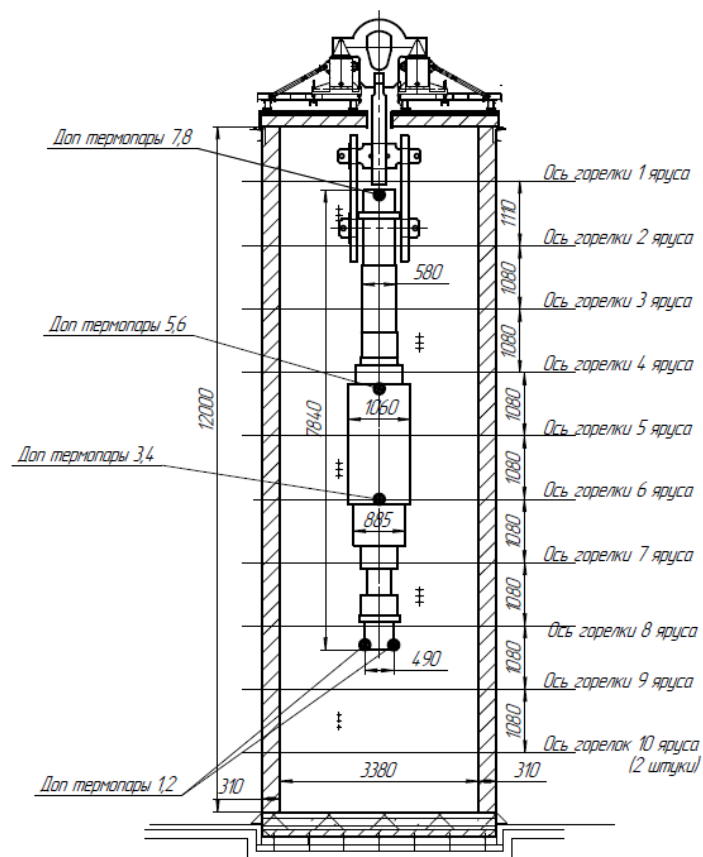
Конструкция печи № 22 с установкой опытного ротора массой 27,26 т, и размещение основных (печных) и дополнительных (на металле) термопар
